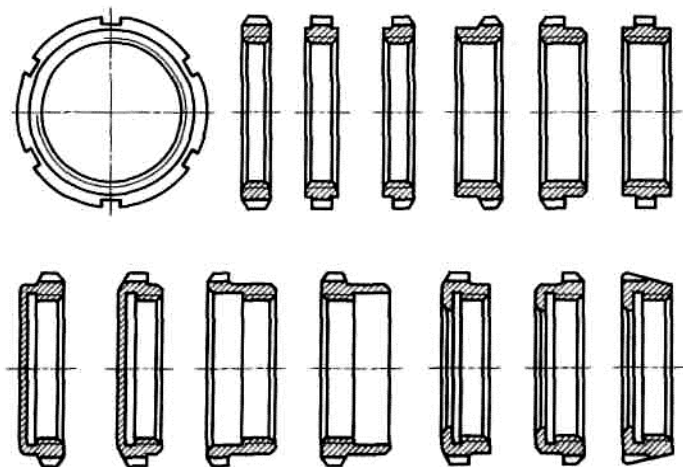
Кольцевые гайки с внутренней резьбой
